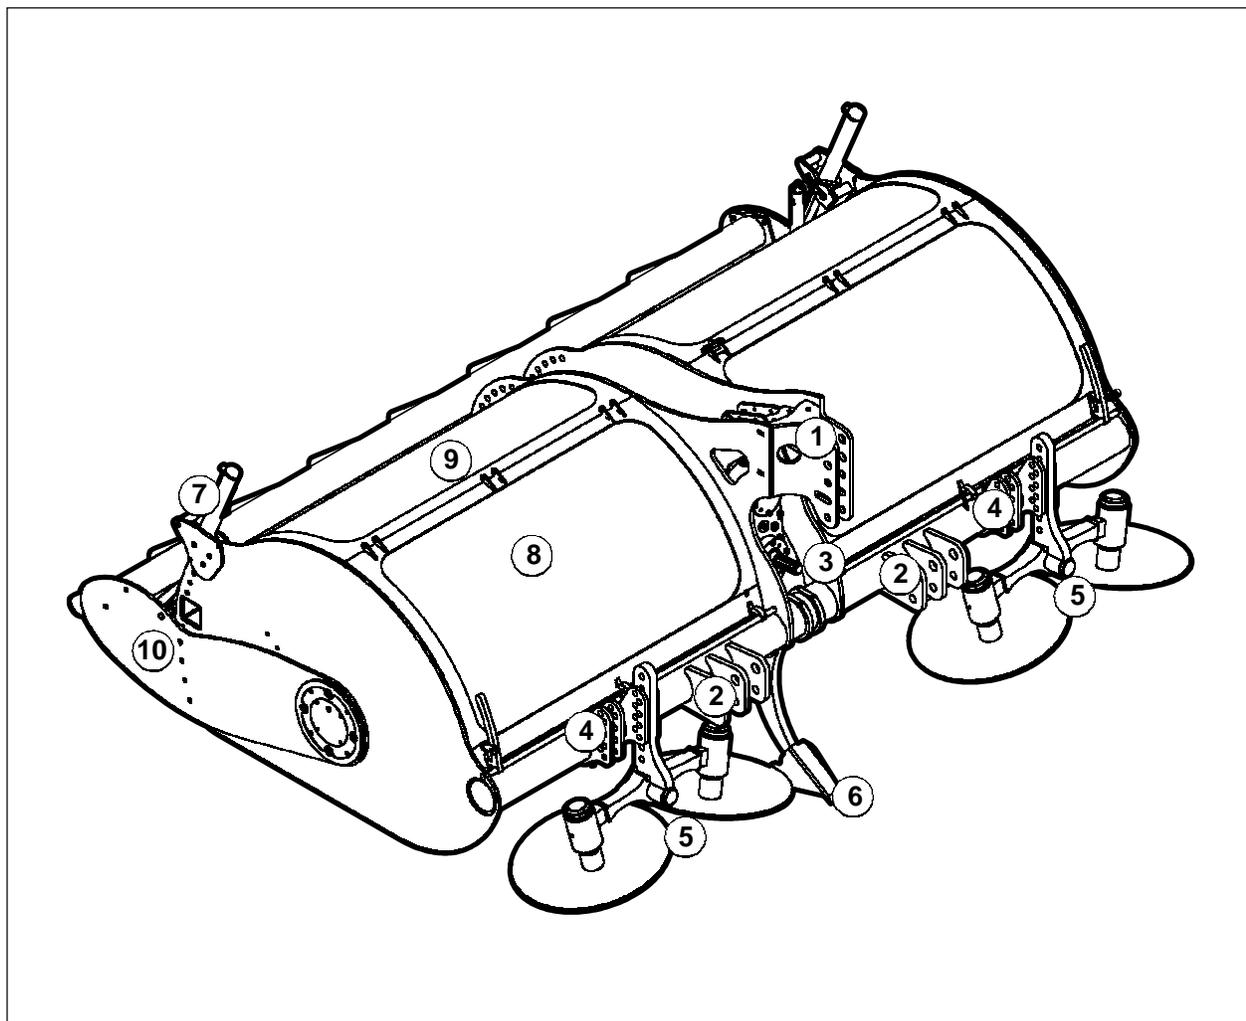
Componenti principali del Rotoaratro-Ripuntatore ROTAR
